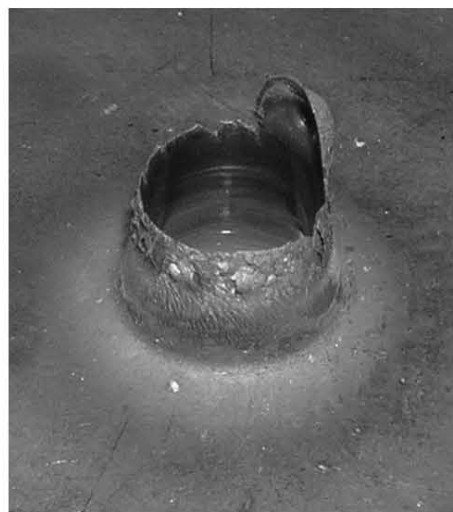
Нижняя часть крепежного элемента (подача 160 мм/мин; инструмент с криволинейной формой рабочей части)
